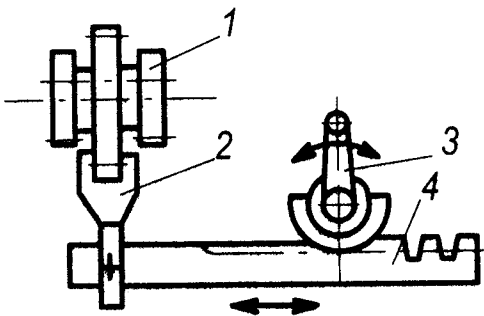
Схема механізму керування блоком зубчастих коліс
